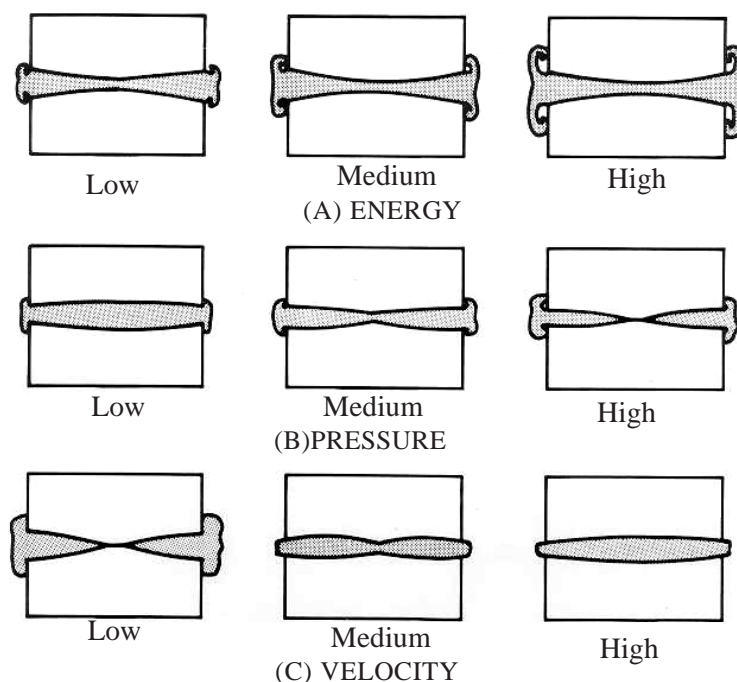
Efeitos dos Parâmetros de Soldagem sobre a Junta.
